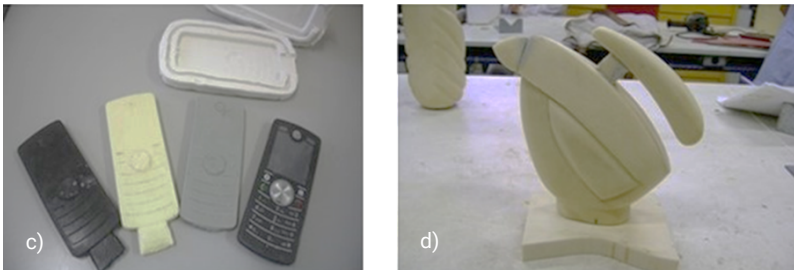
Exemplos (c) e (d) da construção de modelos – oficinas práticas.
